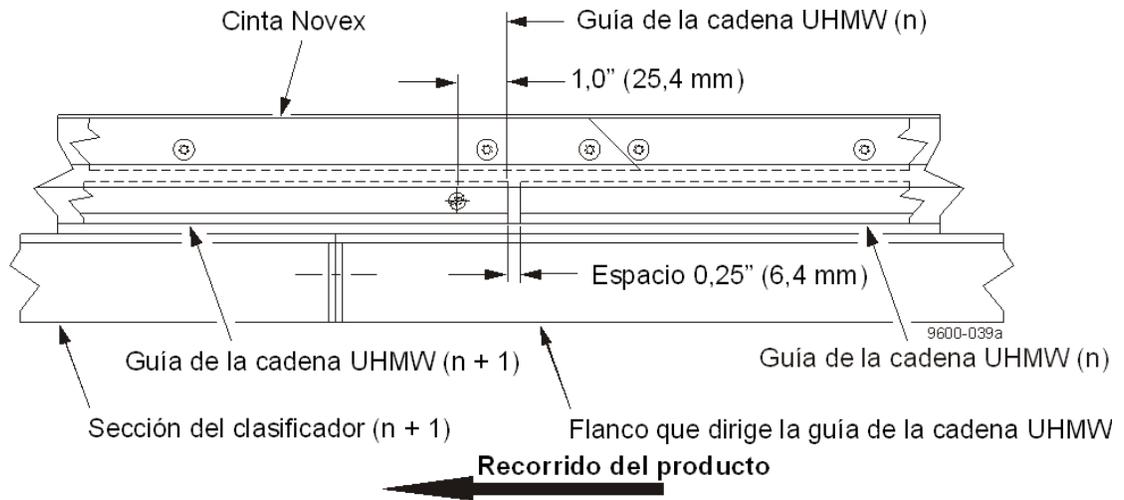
Anclaje de las regletas de la guía de la cadena UHMW
